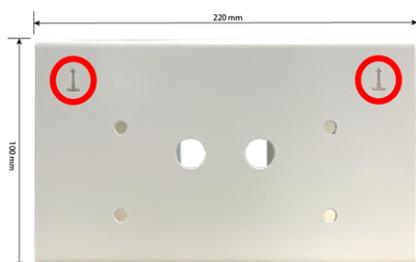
Dimensions MOBOTIX D71 Corner/Pole Mount – vue avant
